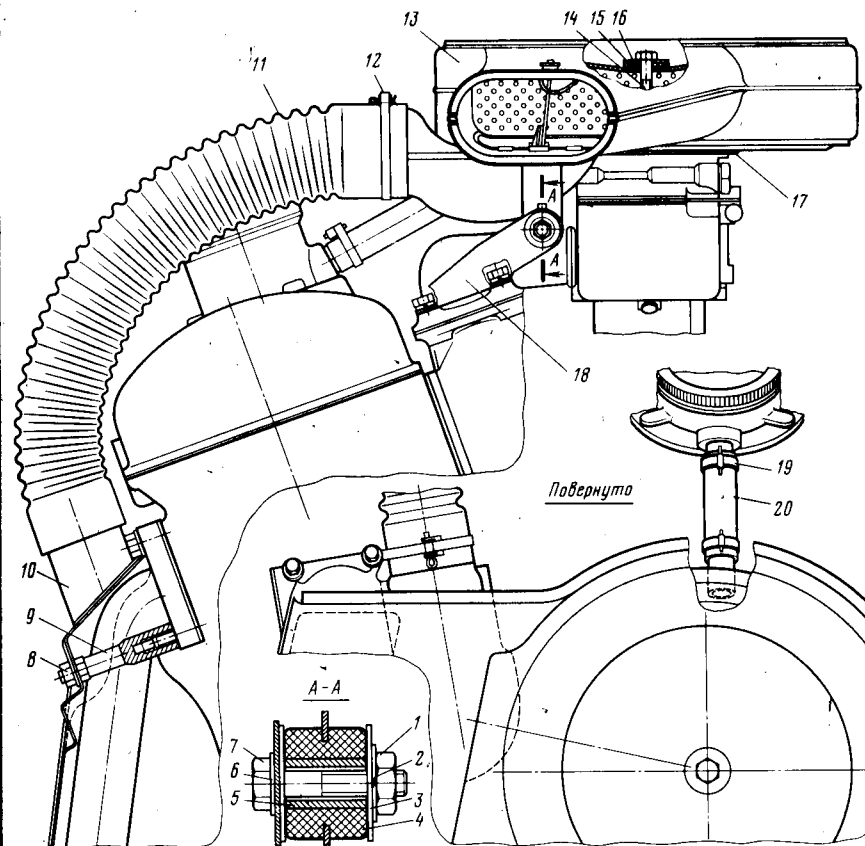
Установка воздушного фильтра на карбюратор К126Н
